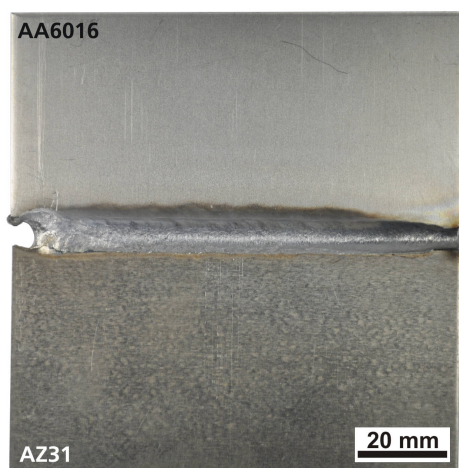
Fotografische Aufnahme der geschweißten coldArc®-Verbindung, AA6016 / AZ31 / AlSi12, Schweißnahtoberseite
